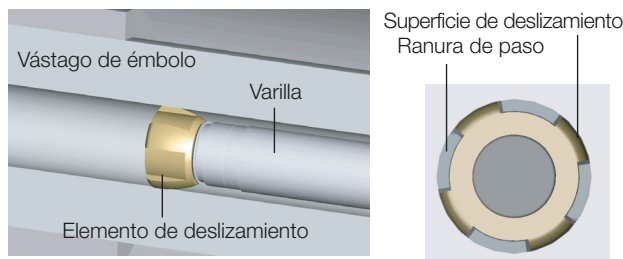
Vista detallada y vista desde arriba del elemento de deslizamiento
